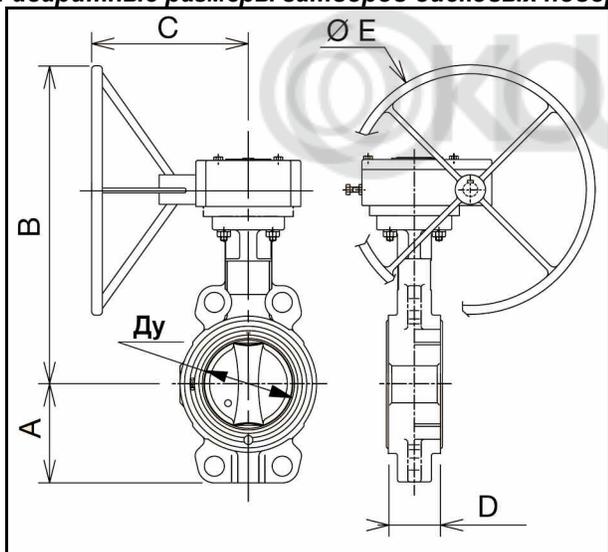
Габаритные и присоединительные размеры затворов дисковых поворотных типа VFY-WG с центрирующими проушинами
